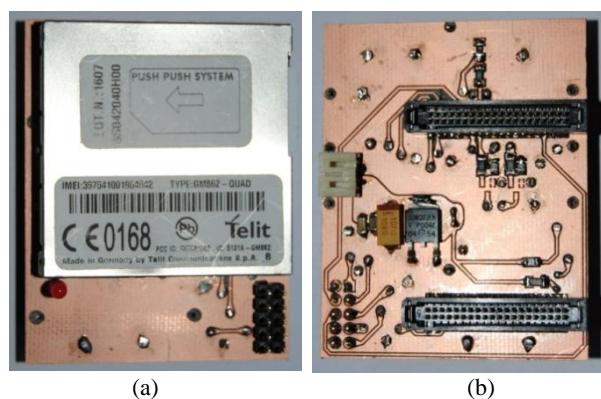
Placa de circuito impreso del módulo GM862 para la conexión al mote, cara *top* (a) y cara *bottom* (b).
